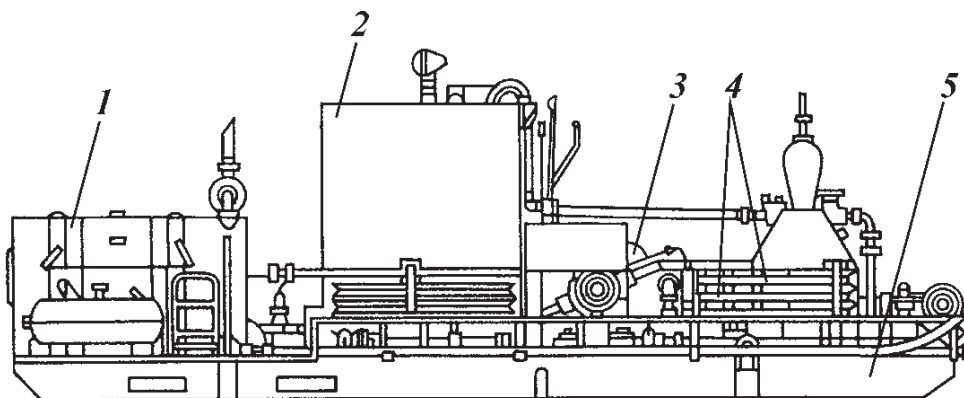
Цементи́ровочный агрегат 5ЦА-320:
